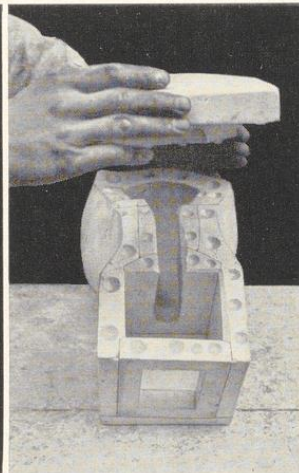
Die zusammengesetzte Form mit dem noch abgehobenen Schlußstück
